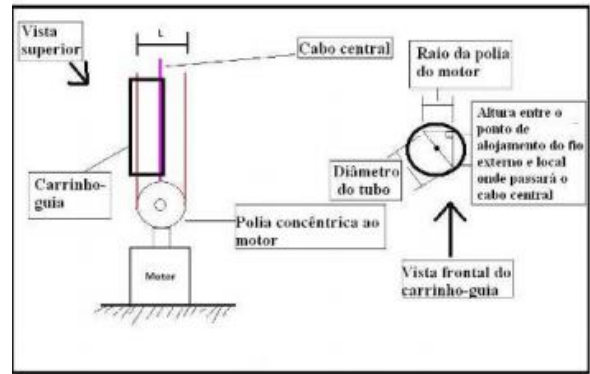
Vista detalhada do arranjo do carrinho-guia.
